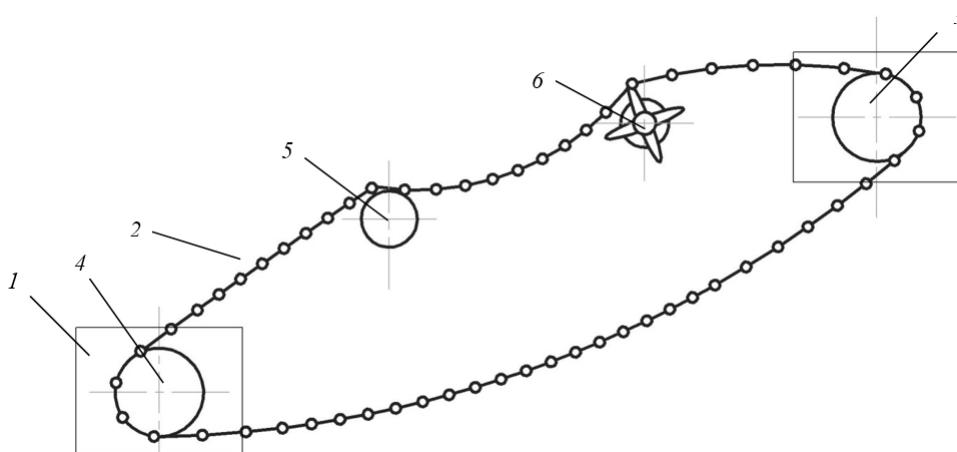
Схема сепарирующего пруткового элеватора с асимметричным расположением встряхивателей: 1 – рама; 2 – прутковый элеватор; 3 – ведущий ролик; 4 – ведомый ролик; 5 – поддерживающий ролик; 6 – встряхиватель
